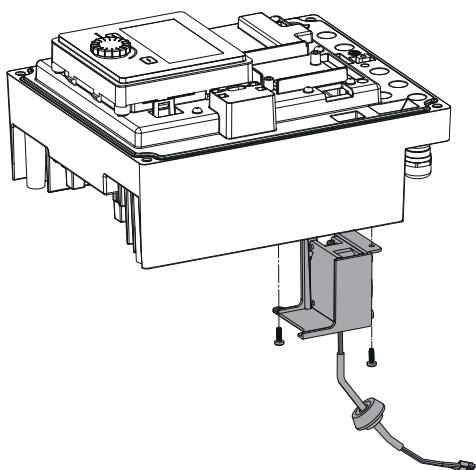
Retirar el ventilador del módulo, incl. el cable y la junta de goma
